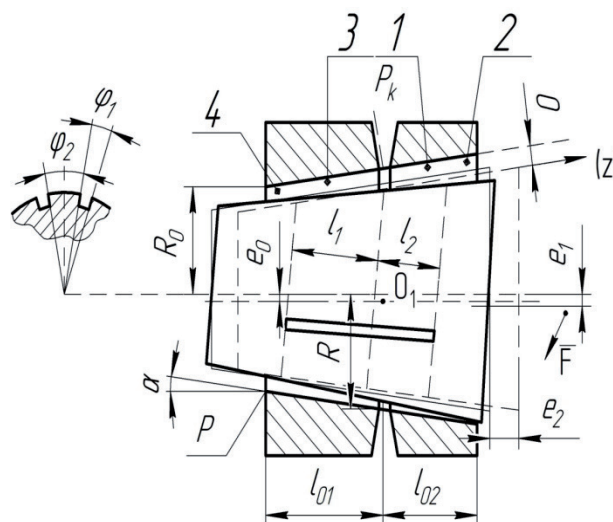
Конічна газостатична опора з канавками змінної глибини
